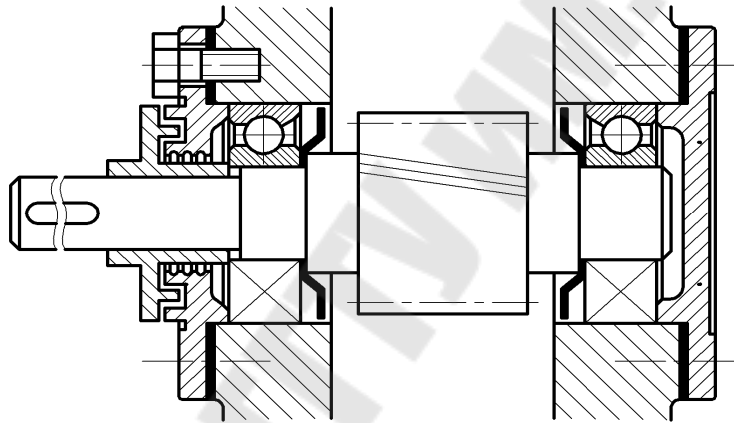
Подшипниковый узел с радиально-упорными шарикоподшипниками, установленными «враспор»
